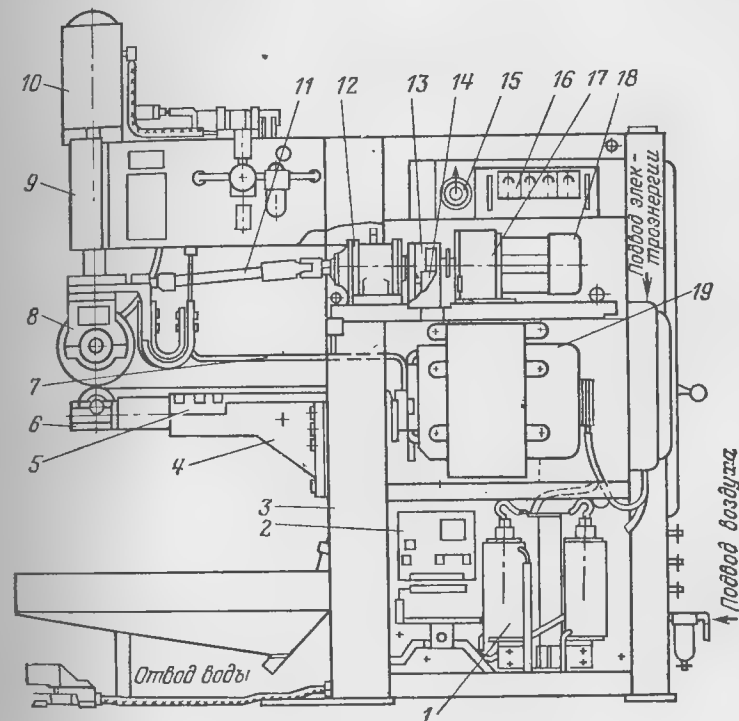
Машина для шовной сварки МШ-3201.
